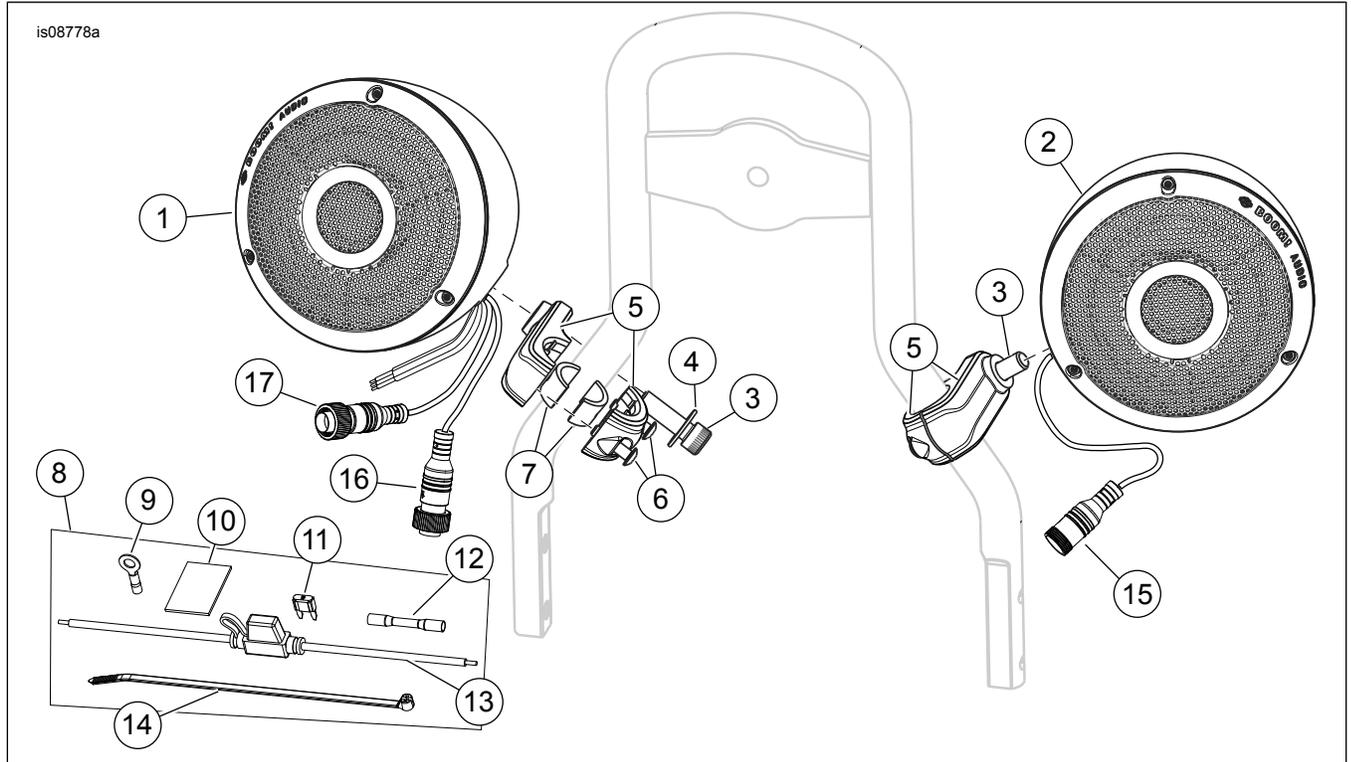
Pièces de rechange, kits de haut-parleurs fixés sur le montant
